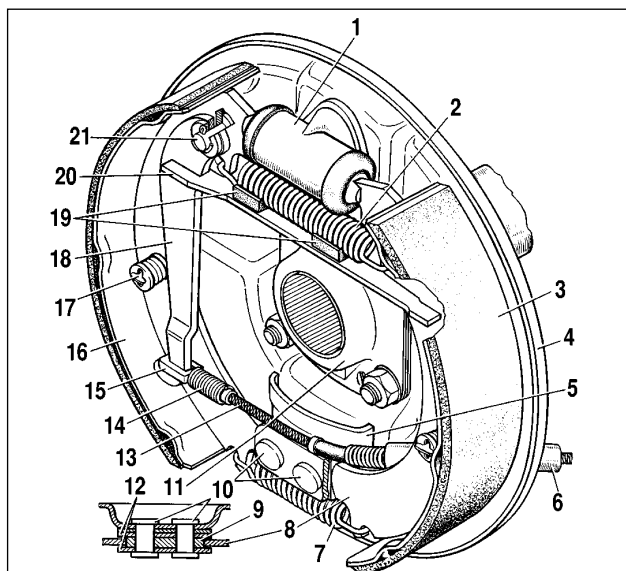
Mécanisme de freinage de la roue arrière :
